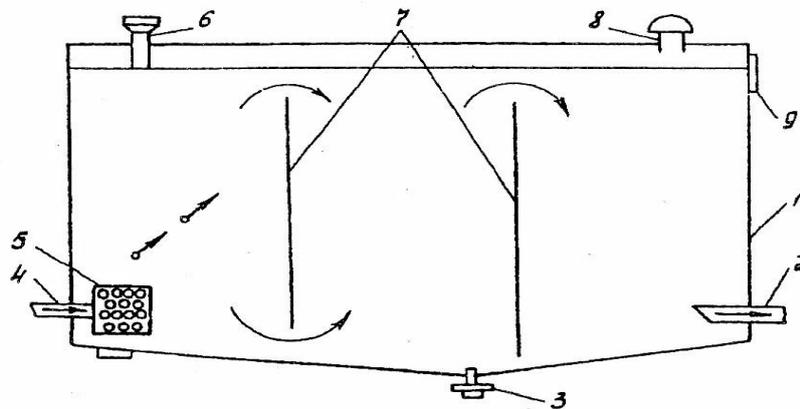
Схема гидробака: 1 – корпус; 2- всасывающий патрубок; 3 – кран слива отстоя; 4 – сливной патрубок; 5 – рассекаватель; 6 – заливная горловина; 7 – перегородки; 8 – воздушный фильтр; 9 – уровнемер
